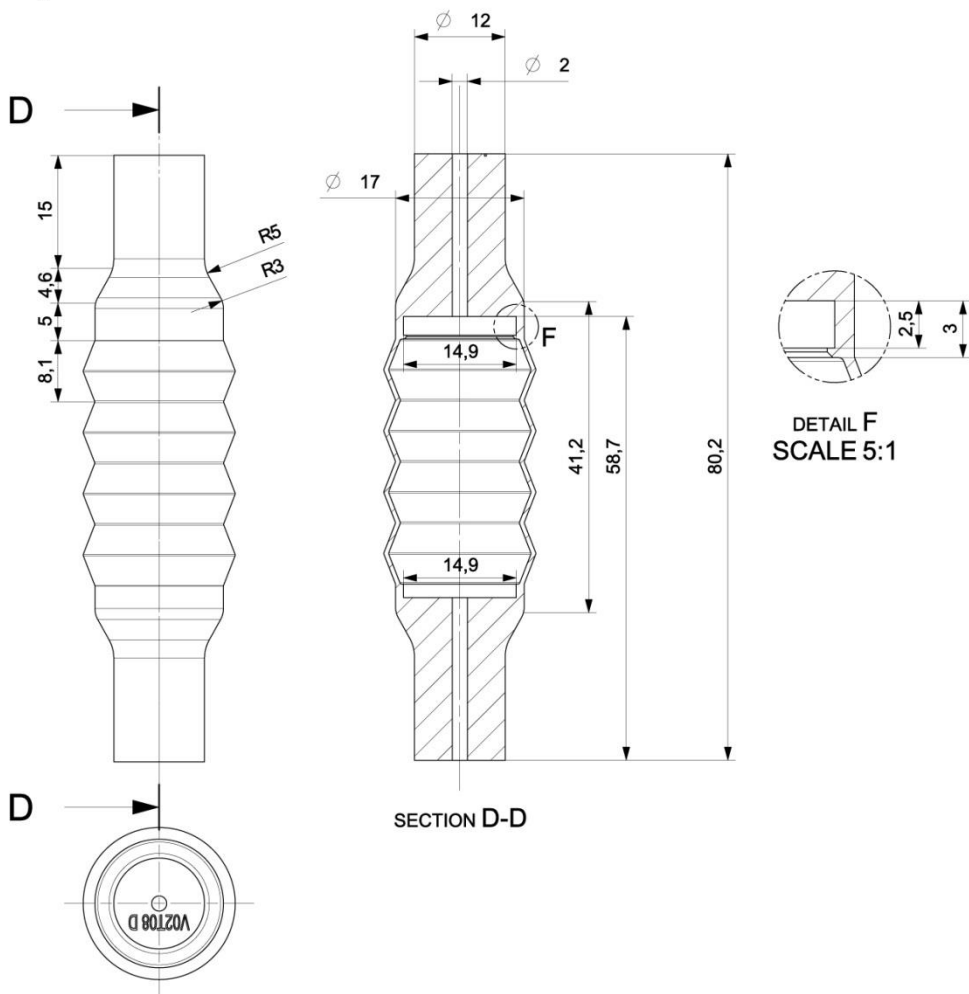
Technische Zeichnung Aktormodulgehäuse V02T08
